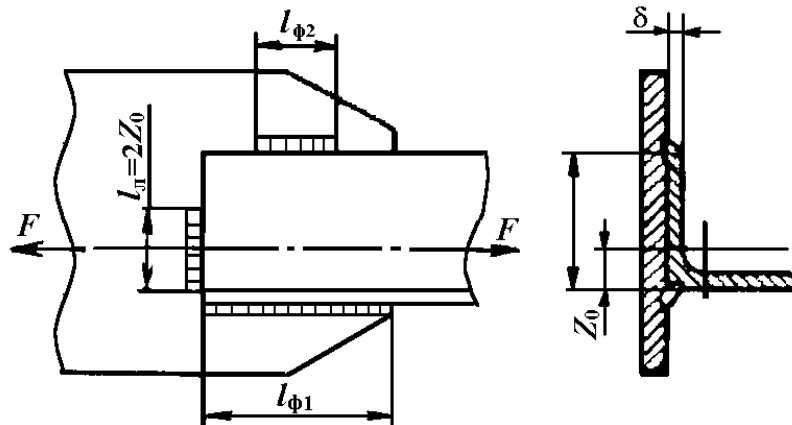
Сварное соединение уголка с косынкой
